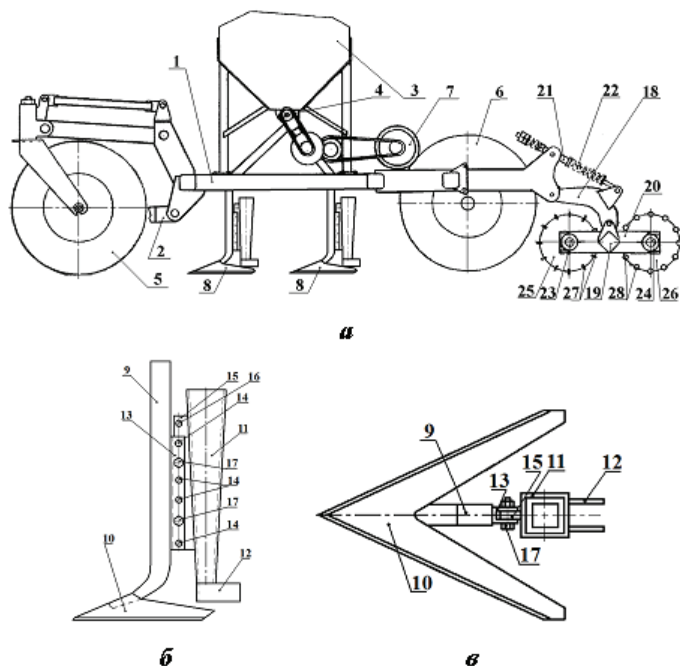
Схема зерновой сеялки (обозначения в тексте): а – вид сбоку зерновой сеялки; б – сошник (вид сбоку); в – сошник (вид сверху)
